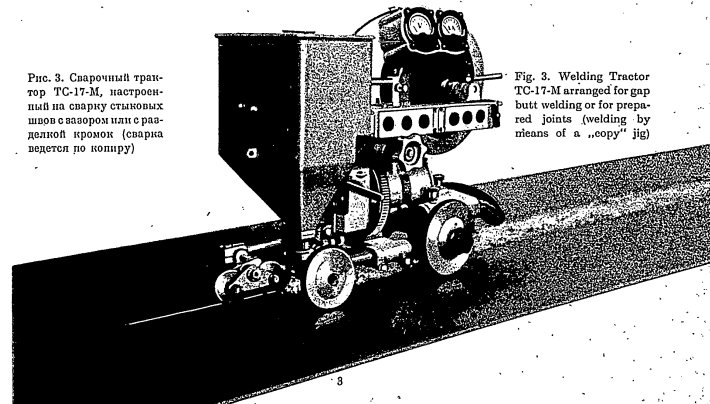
Сварочный трактор TC-17-M, настроенный на сварку стыковых швов с зазором или с разделкой кромок (сварка ведется по копрю)
